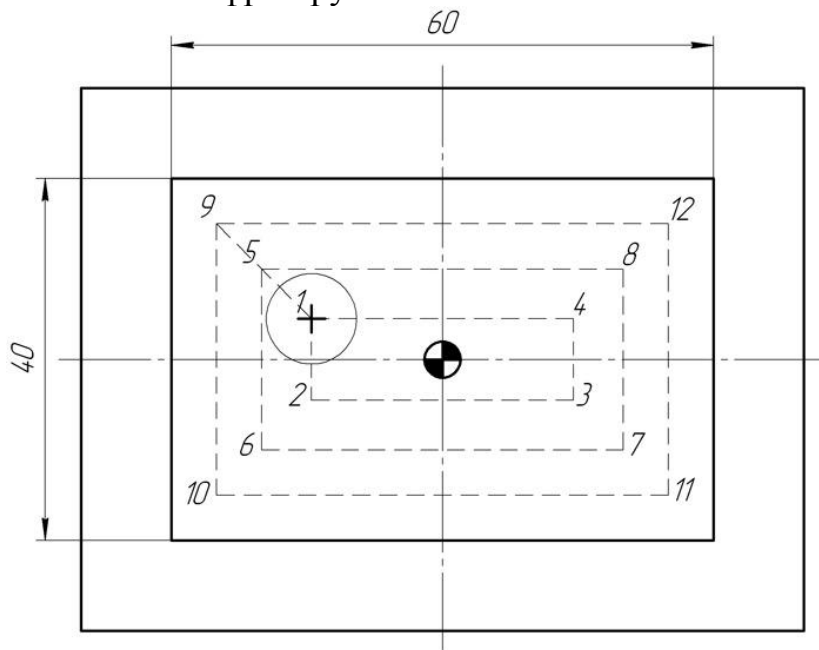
Чорнове фрезерування прямокутної кишені
